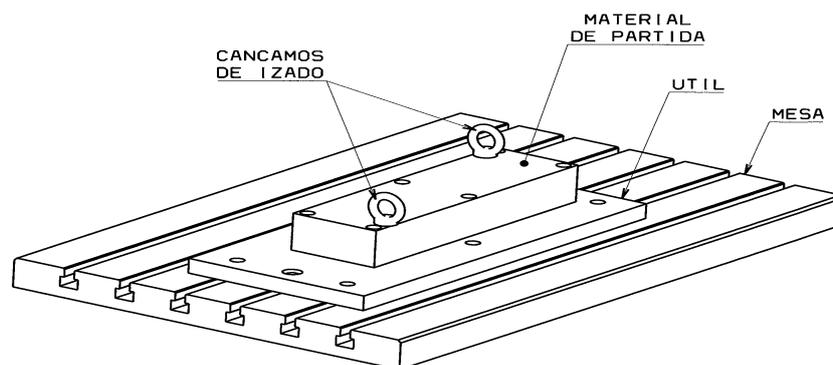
Taladros de izado en una máquina de mesa horizontal
